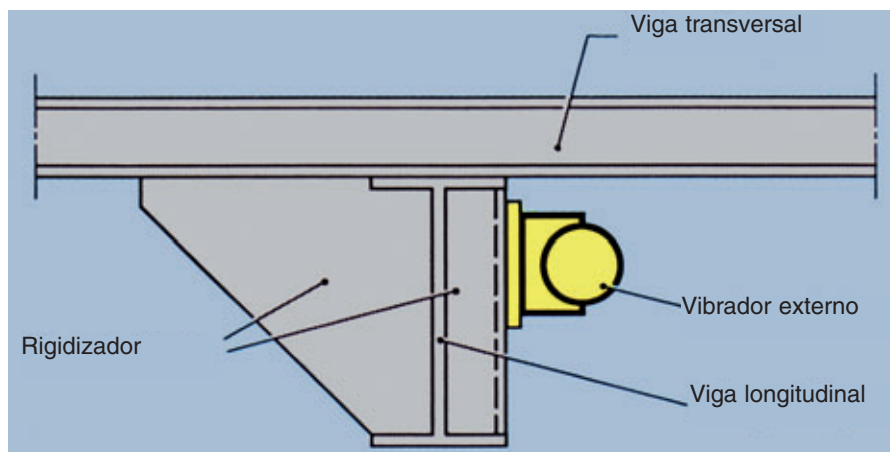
Montage con refuerzo de un vibrador en la viga longitudinal de una mesa vibratoria grande
